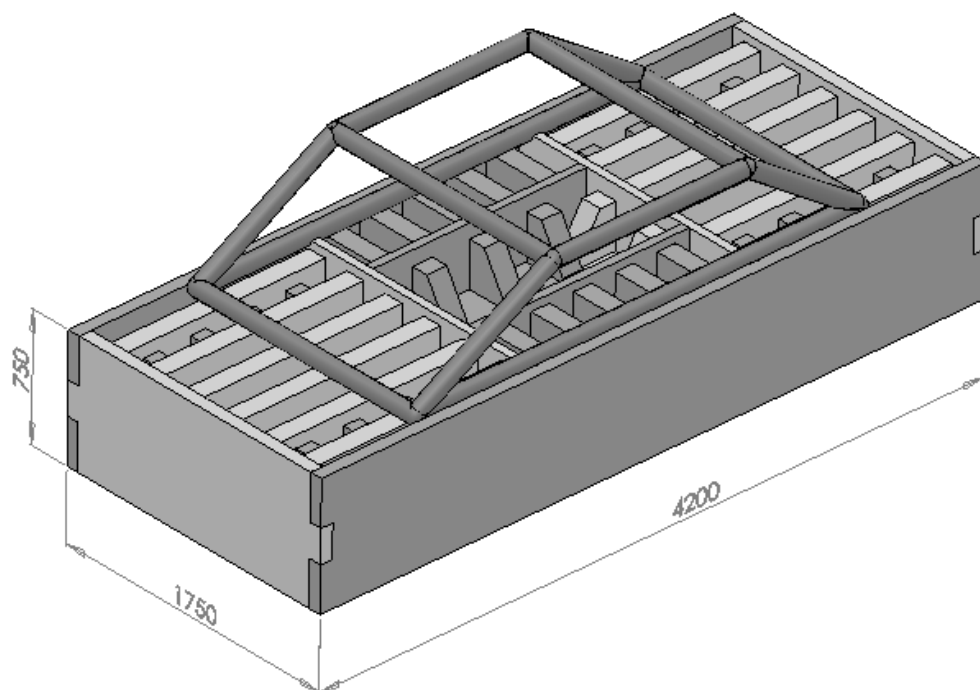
Carrosseria del *balloon car* amb les seves principals dimensions
